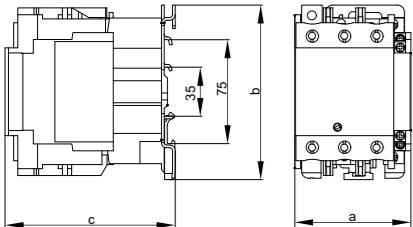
Габаритные размеры контакторов КМИ-А-46512 – КМИ-А-49512
